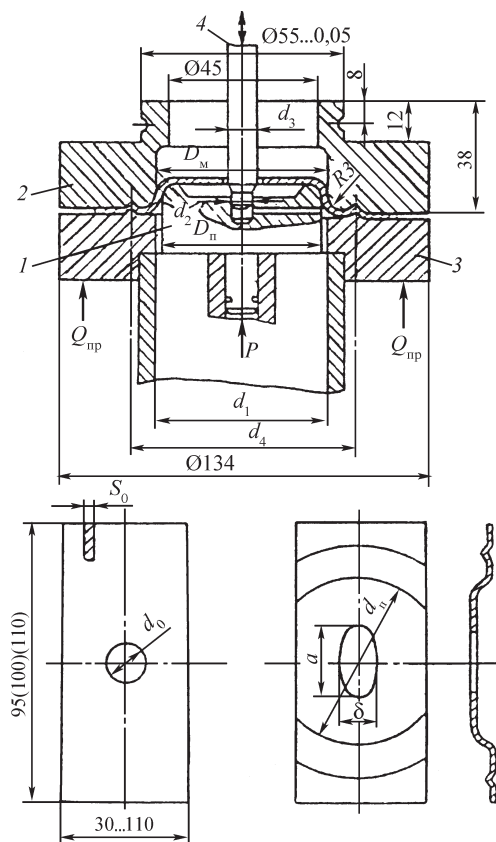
Штамповая оснастка для испытаний листового металла на машине МТЛ-10Г и образцы для отбортовки полос с центральным отверстием
